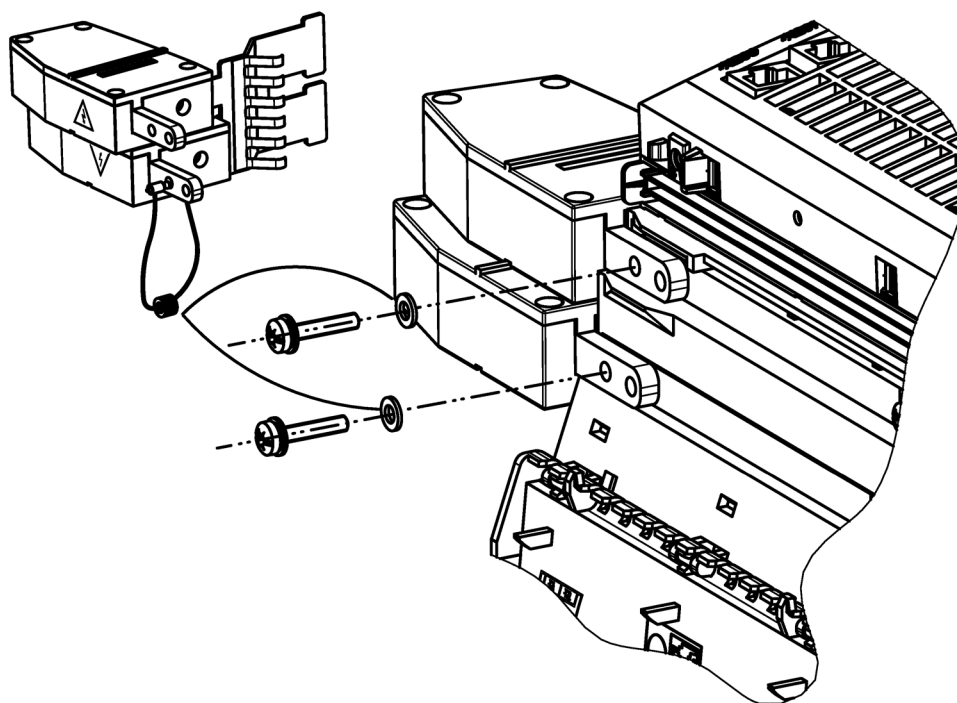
Montaje del adaptador de circuito intermedio en el lado izquierdo con 2 tornillos para anchos de módulo de 150 a 300 mm
